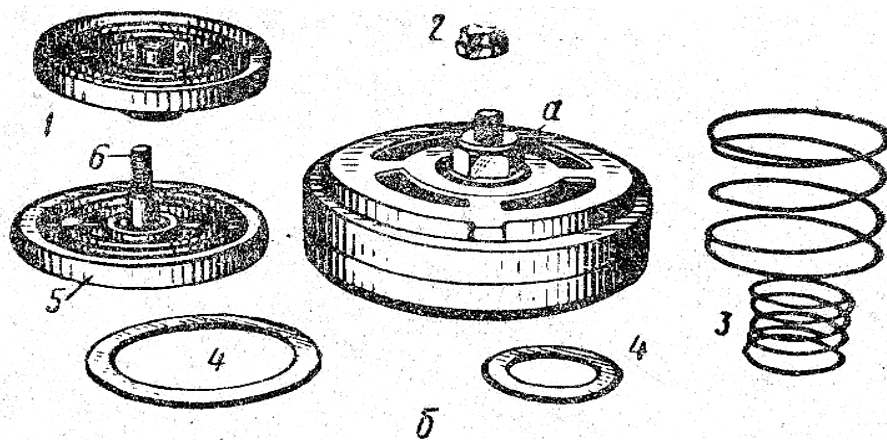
Кольцевой пластинчатый клапан поршневого компрессора
